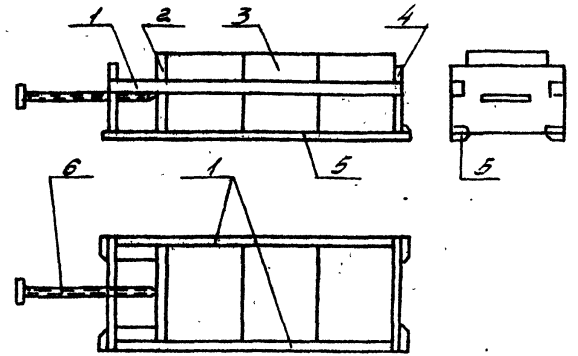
Схема приспособления для обжатия контрольных образцов. 1 - направляющие; 2 - подвижная перевертка; 3 - схватываемые кубы; 4 - торцевой упор; 5 - подбашка; 6 - винт.
